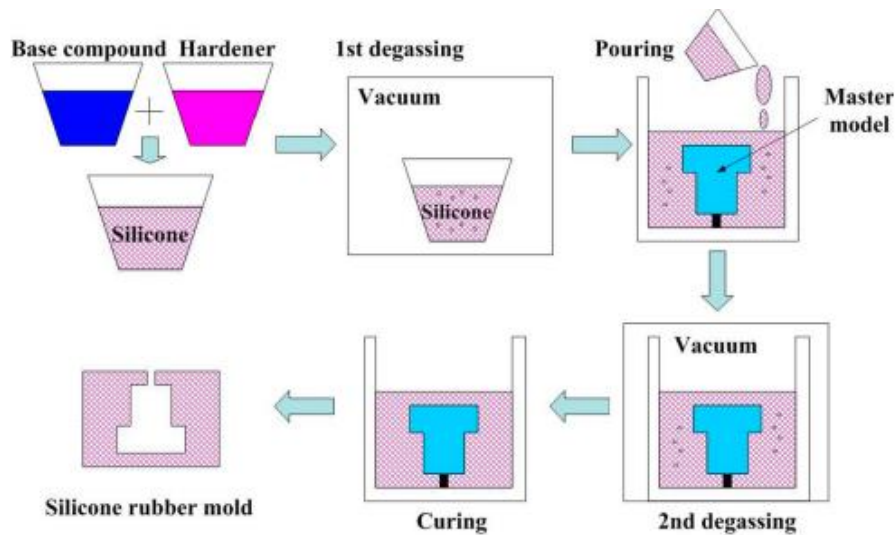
Proceso de vacuum casting (Kuo & Wu, 2017).
